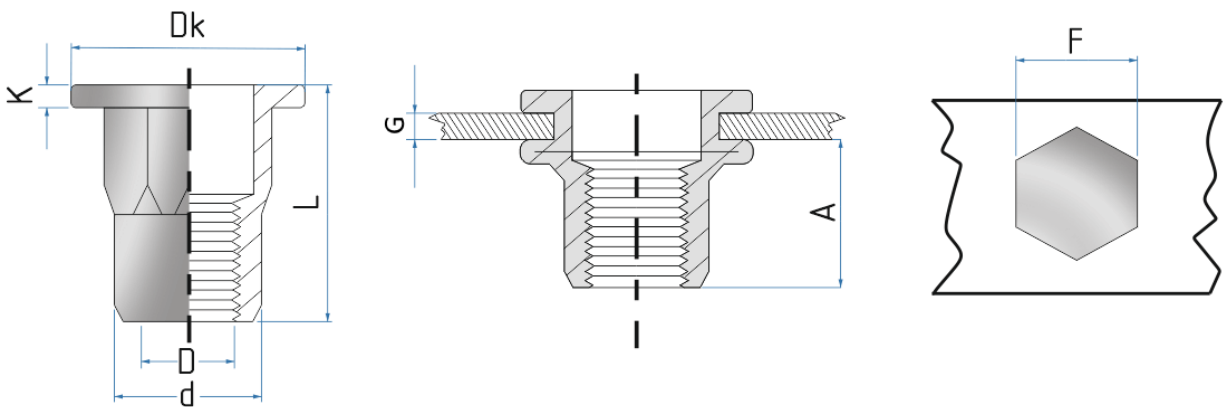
Заклёпка резьбовая полушестигранная, стандартный борт,
